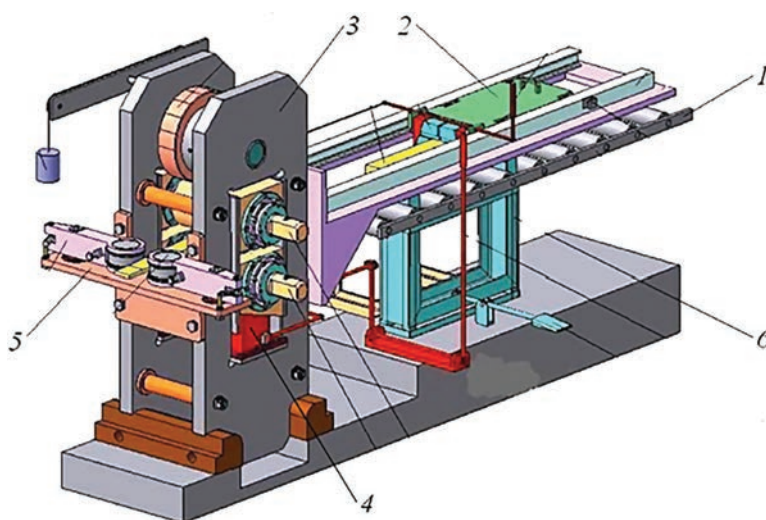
Схема опытного стана для прокатки малолистовых рессор: 1 – приводной рольганг для перемещения заготовки от нагревательной печи к стану; 2 – подвижная каретка для подачи заготовки в валки; 3 – прокатная клетка; 4 – устройство для регулировки зазора между валками; 5 – устройство для обжатия полосы по ширине; 6 – устройство для подъема заготовки с уровня рольганга до уровня подвижной каретки
